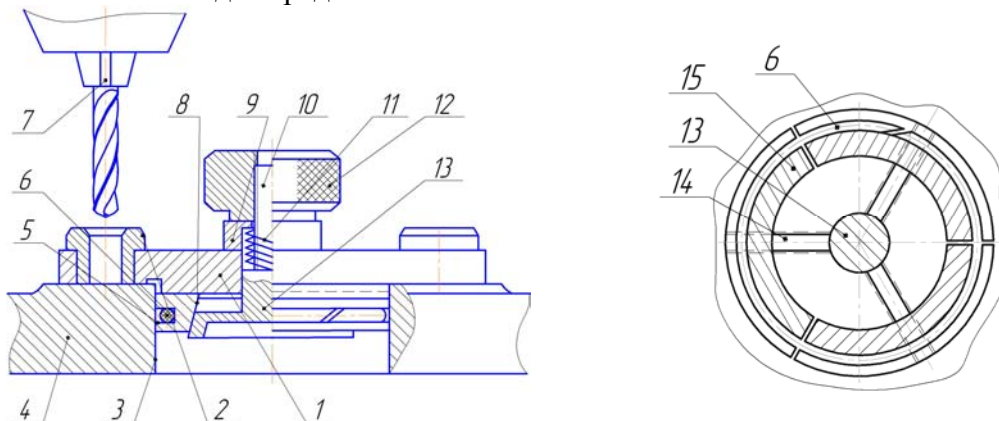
Накладний переналагоджувальний сверлильний кондуктор
